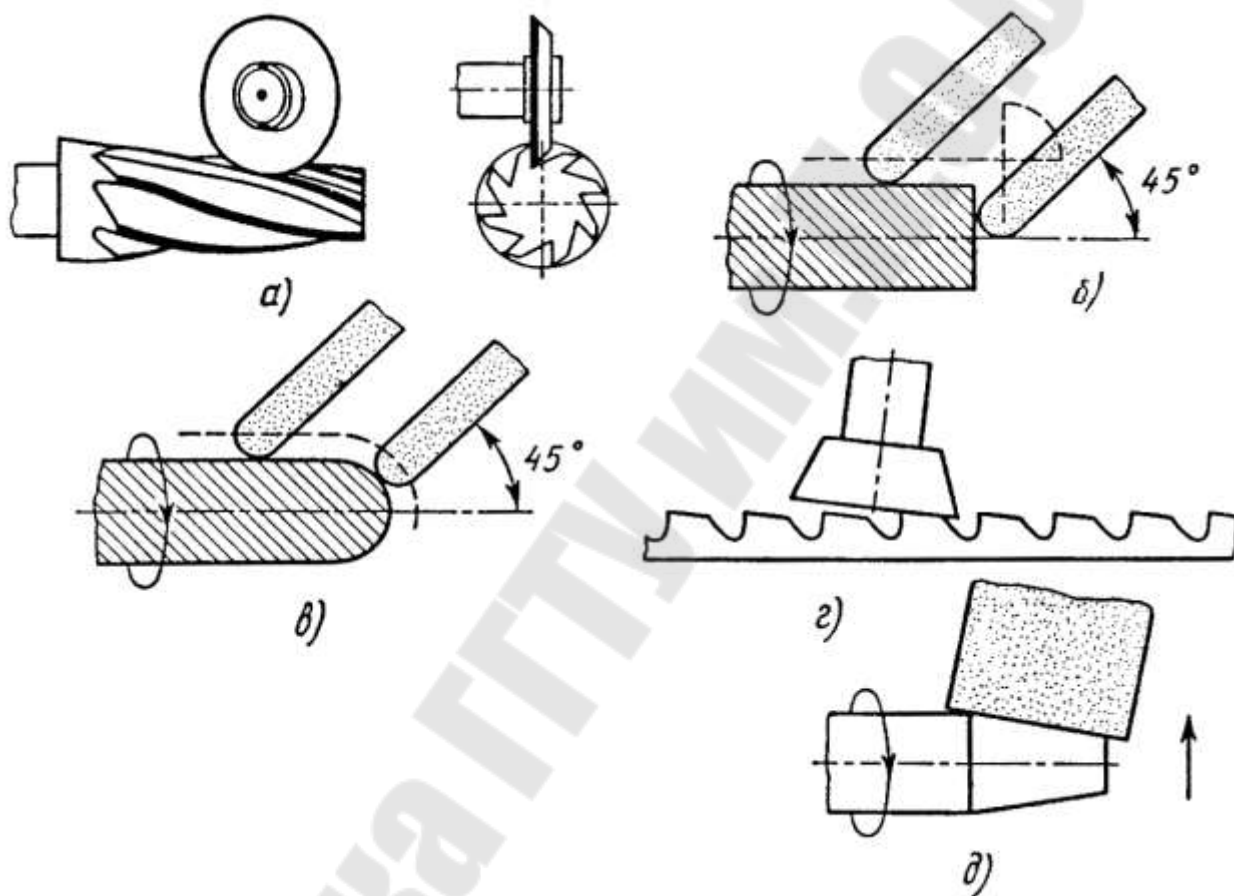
Схемы заточки на заточном станке с ЧПУ многолезвийного инструмента: а – конической концевой фрезы по передней поверхности зуба тарельчатым инструментом; б – цилиндрической концевой фрезы по задним поверхностям винтового и торцового зубьев тороидальным инструментом; в – концевой фрезы со сферическим концом по задним поверхностям винтового и радиусного зубьев тороидальным инструментом; г – плоской протяжки по задней поверхности чашечным инструментом; д – метчика по задней поверхности режущей части инструментом прямого профиля (затылование заборного конуса)
